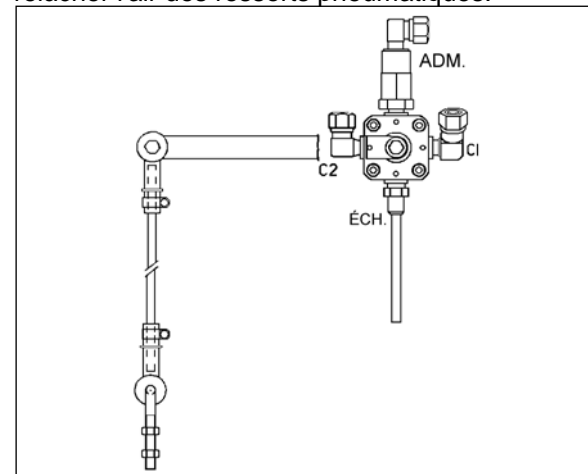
SOUPE DE COMMANDE DE HAUTEUR 16093
